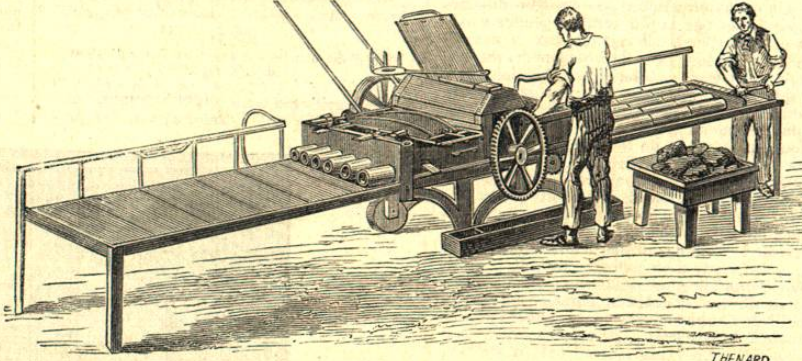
Machine de Whitehead pour fabriquer les tuyaux de drainage.
